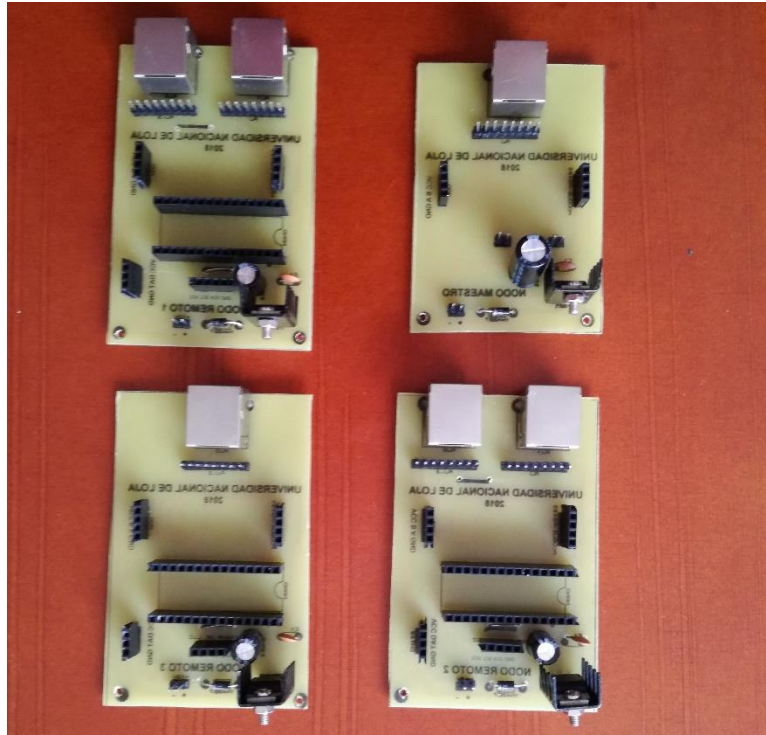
Placas PCB terminadas. Fuente [El Autor]
